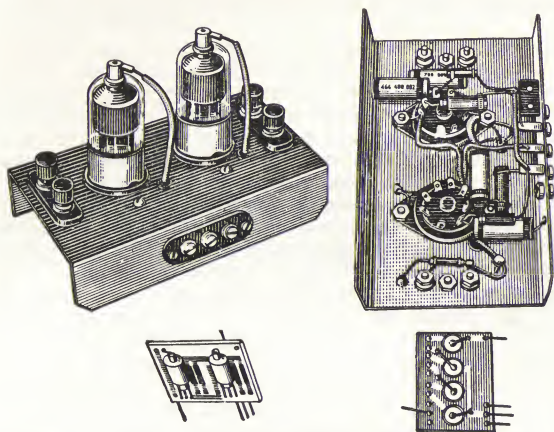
Двухламповые усилители: сверху — объёмной конструкции с нормальными лампами; внизу — печатной конструкции с малогабаритными лампами (слева — вид сверху, справа — вид снизу).
